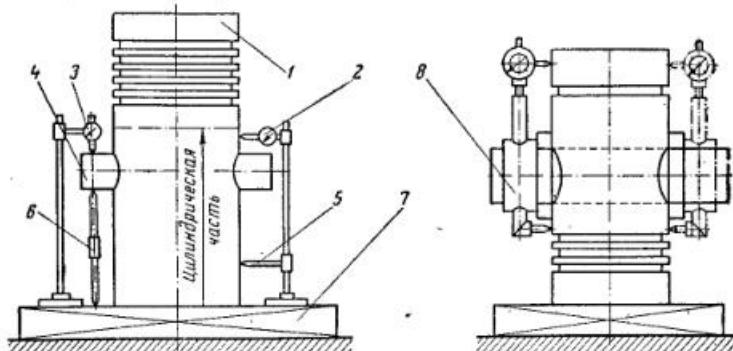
Проверка перпендикулярности осей отверстия под поршневой палец и поршня с помощью индикатора и микрометрического штихмасса:
